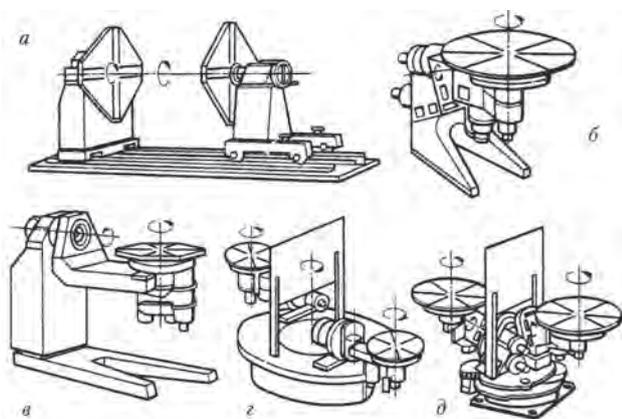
Манипуляторы изделия с программным управлением для оснащения робототехнологического комплекса для дуговой сварки: а – сварочные горизонтальные двухстоечные вращатели - 402М и М150530; б, в – сварочные универсальные вращатели - М150400 и М150500; г, д – сварочные универсальные двухпозиционные вращатели - М150310 и М150410
